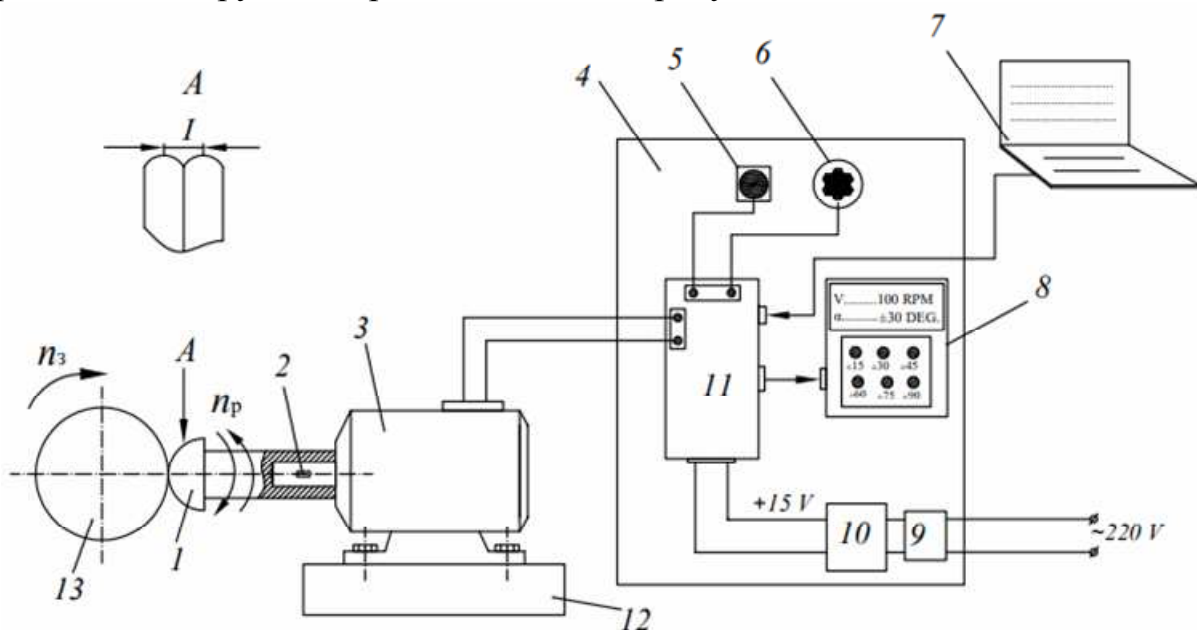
Принципиальная схема устройства для создания реверсивного кругового движения рабочего инструмента: 1 – рабочий инструмент; 2 – шпонка; 3 – шаговый электродвигатель; 4 – блок управления; 5 – кнопка запуска; 6 – регулятор скорости реверса; 7 – персональный компьютер; 8 – экран режимов обработки; 9 – автоматический выключатель; 10 – трансформатор; 11 – программируемый контроллер; 12 – основание, 13 – заготовка
